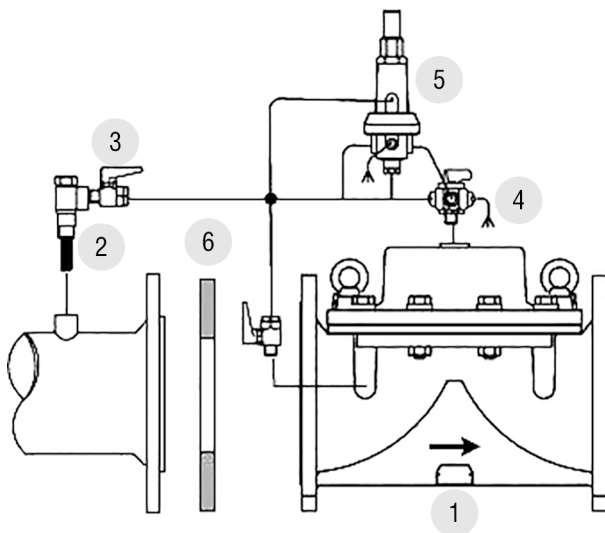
СХЕМА РЕГУЛЯТОРА РАСХОДА: 1 — БАЗОВЫЙ КЛАПАН; 2 — САМОПРОМЫВАЮЩИЙСЯ ФИЛЬТР; 3 — КОНТРОЛЬНЫЙ КЛАПАН*; 4 — РУЧНОЙ 3-ХОДОВОЙ СЕЛЕКТОР*; 5 — 3-ХОДОВОЙ ПИЛОТНЫЙ РЕГУЛЯТОР (ДРУГИЕ ТИПЫ ПО ТРЕБОВАНИЮ); 6 — ШАЙБА С КАЛИБРОВАННЫМ ОТВЕРСТИЕМ.
